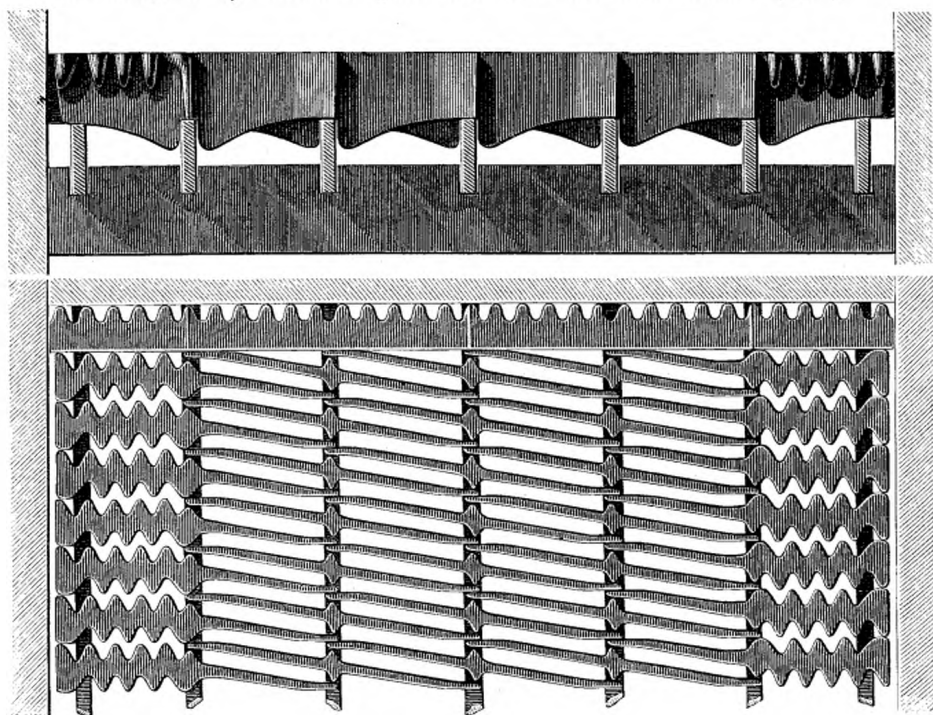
PLAN DE GRILLE SECTIONNELLE.
